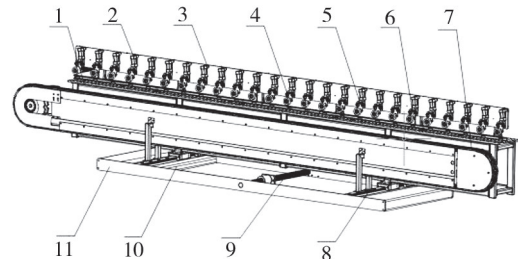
被动式木窗双端铣削加工定位夹紧装置总体布局图
